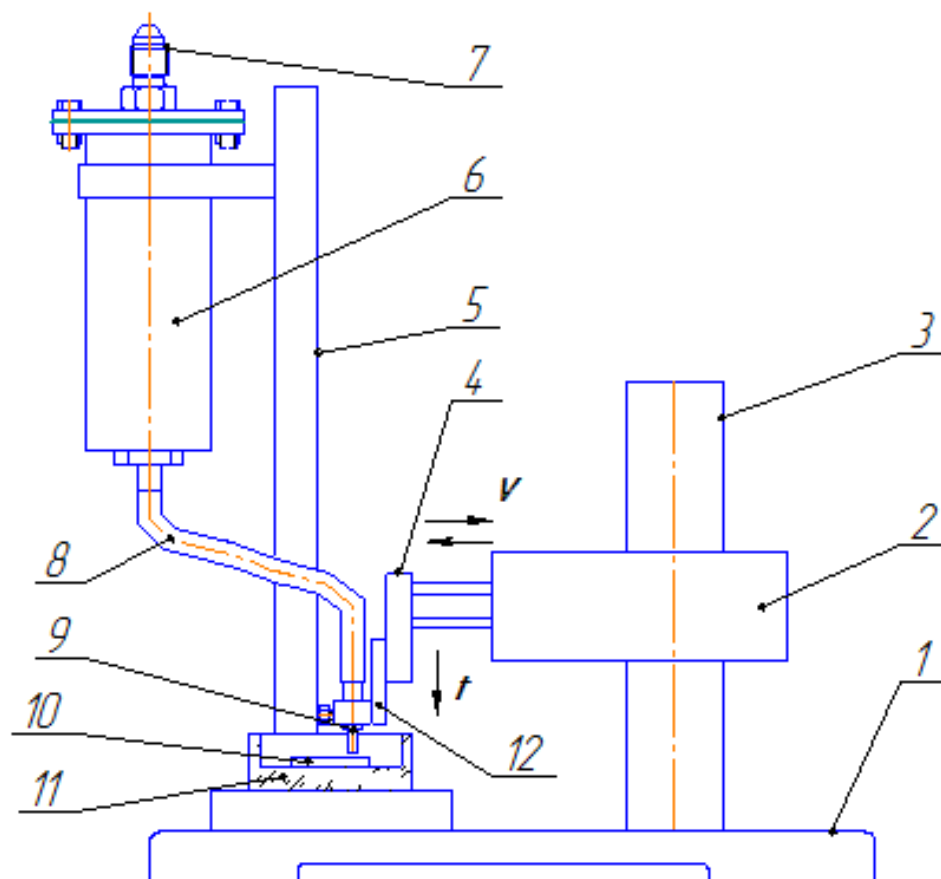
Схема экспериментальной установки для электрохимической струйной обработки: 1 – основание; 2 – приводной блок; 3 – стойка; 4 – каретка продольного хода; 5 – штатив; 6 – емкость для электролита; 7 – штуцер для подачи воздуха; 8 – шланг; 9 – катодинструмент; 10 – деталь; 11 – электрохимическая ячейка; 12 – каретка вертикального перемещения.
